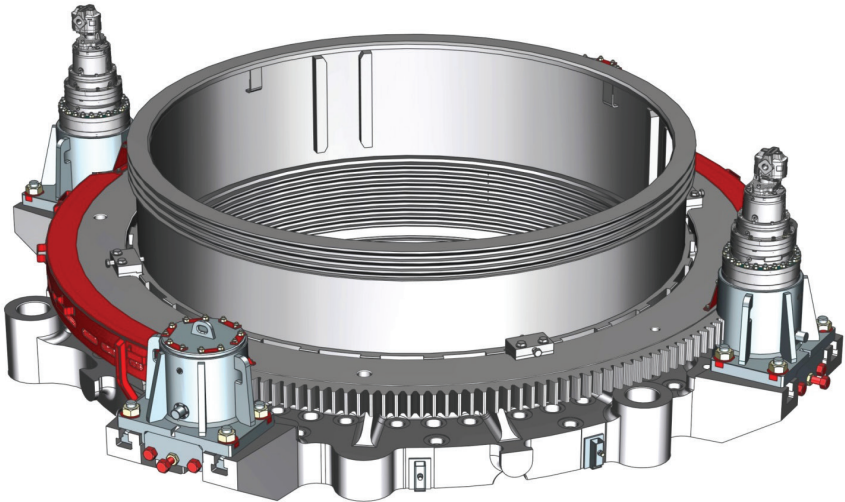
Зубчатый реверсивный механизм регулирования щели дробилки
